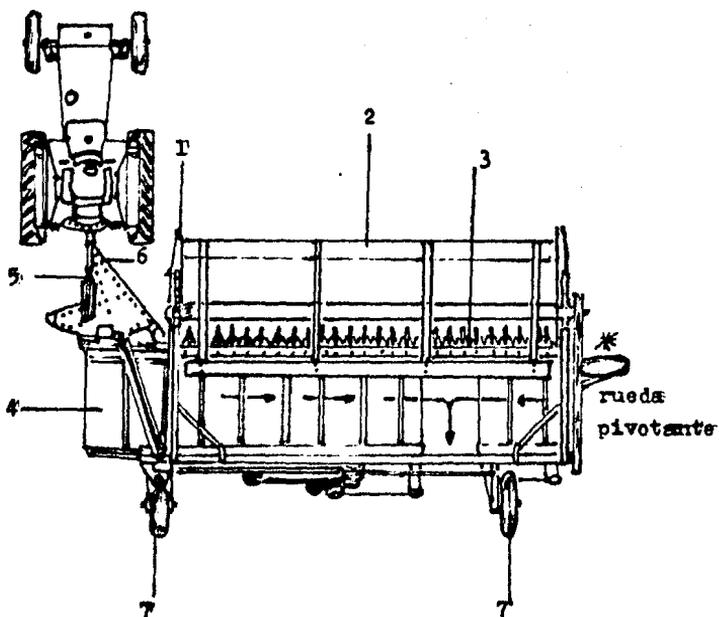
SEGADORA-HILERADORA TIPO REMOLQUE
